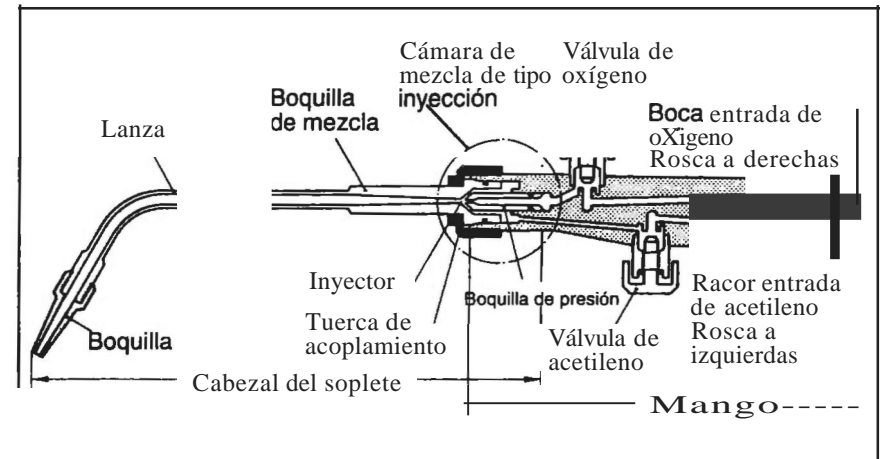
SOPLETE DE INYECCIÓN PARA SOLDEO OXIACETILÉNICO
